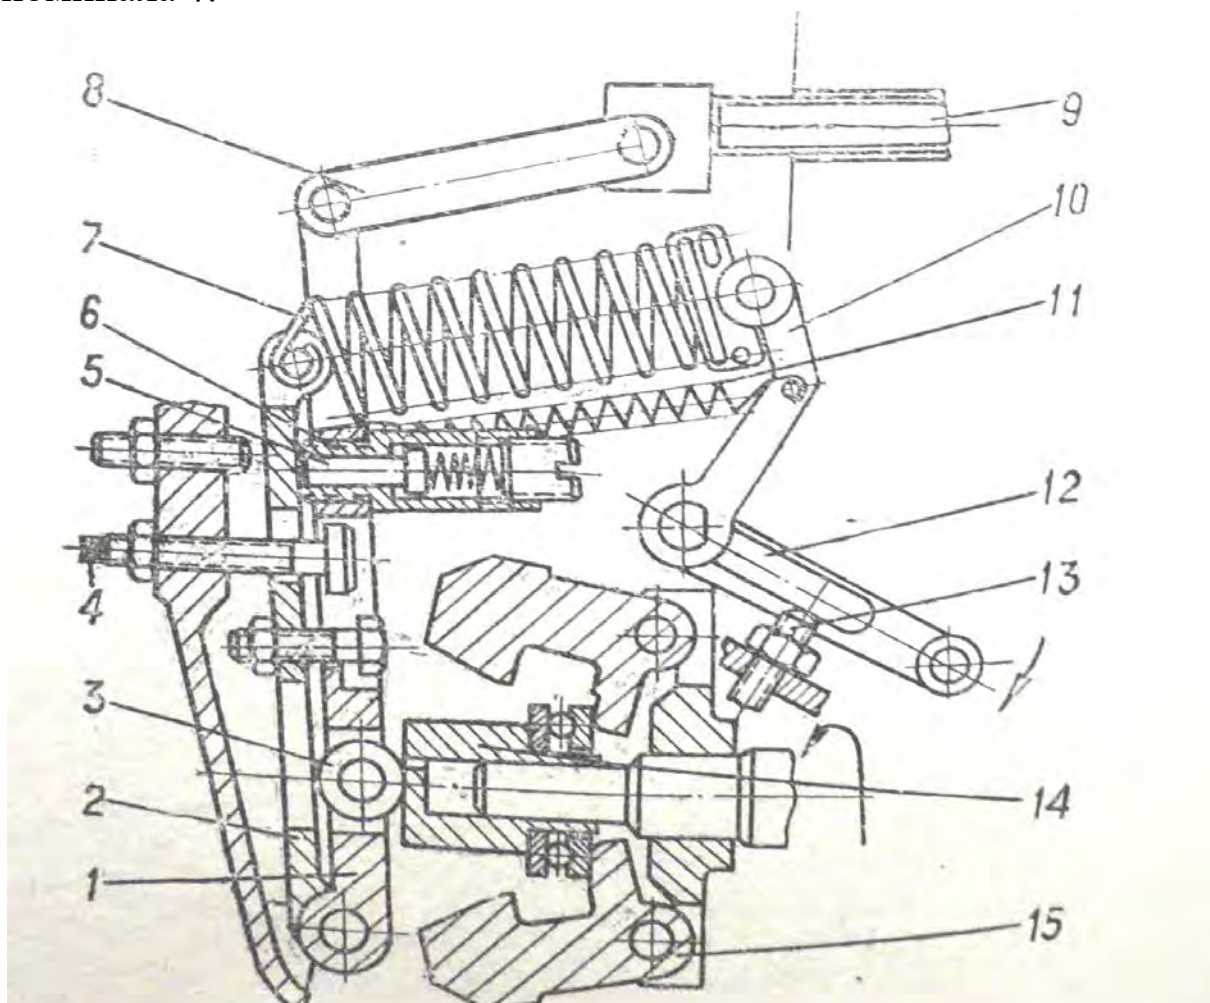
Схема работы регулятора при номинальной нагрузке двигателя:
